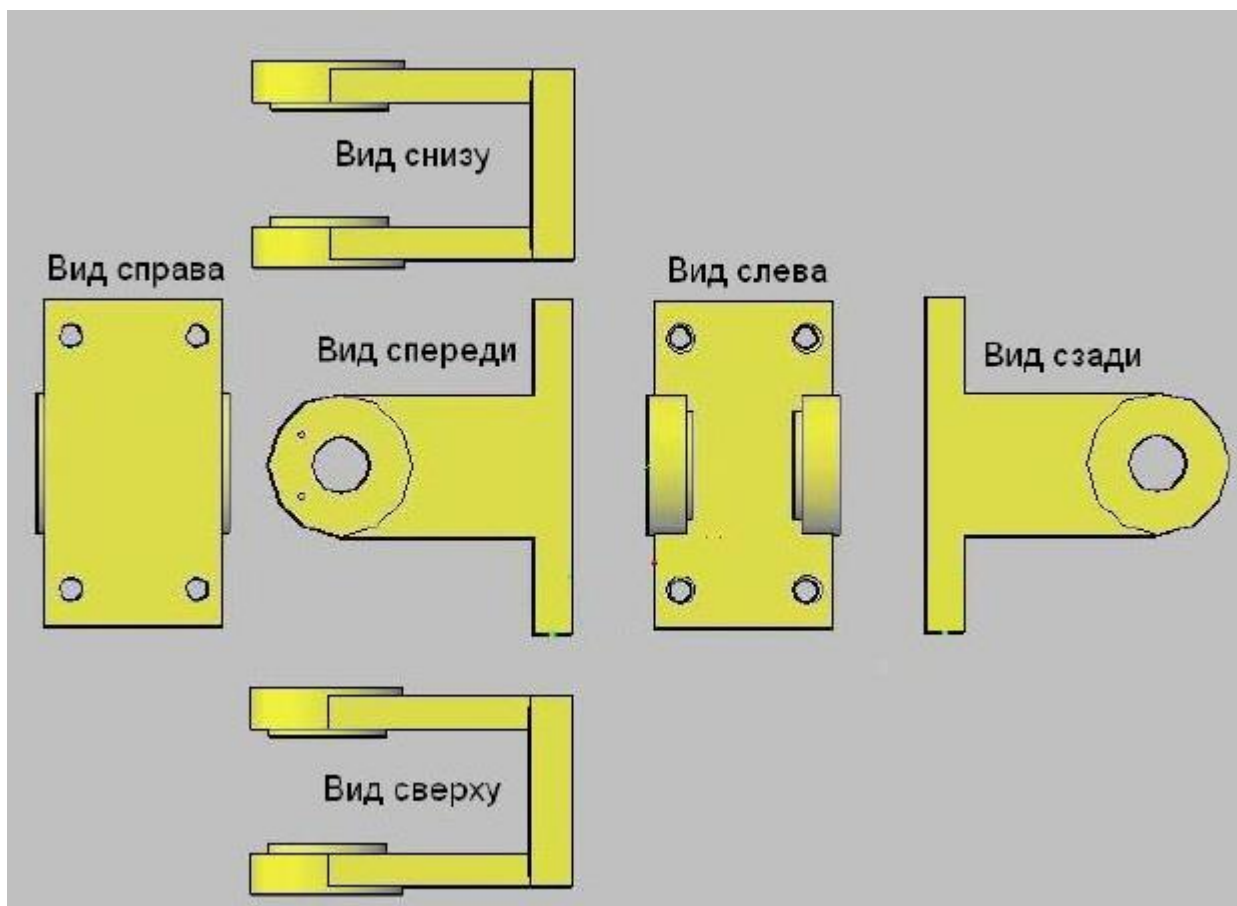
Расположение видов чертежа "Вилка" по ГОСТ 2.305-68
